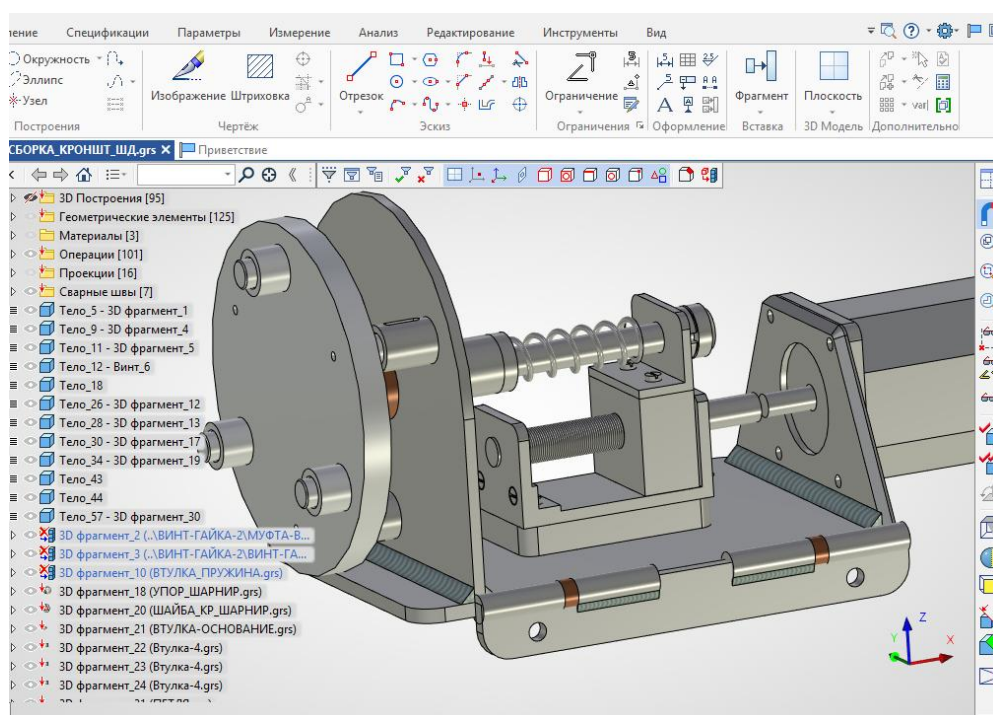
Общий вид разработанного модуля закрепления и прижима образцов
